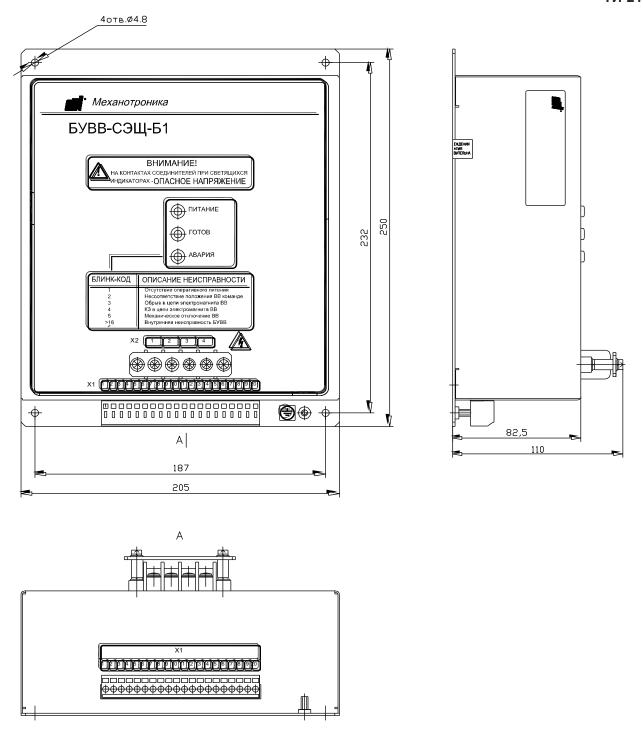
Вид общий БУВВ-Т, габаритные и установочные размеры
